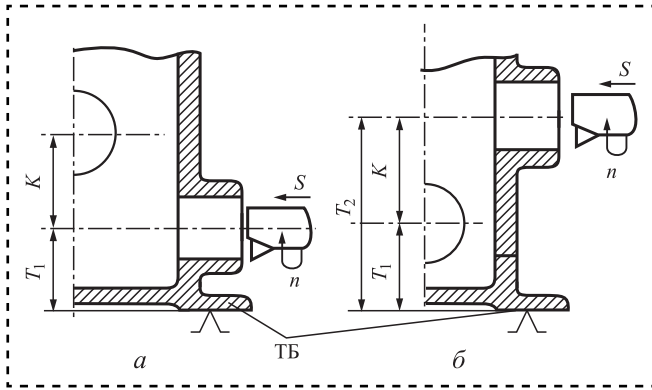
Схемы обработки отверстий под подшипники в корпусе червячного редуктора:
